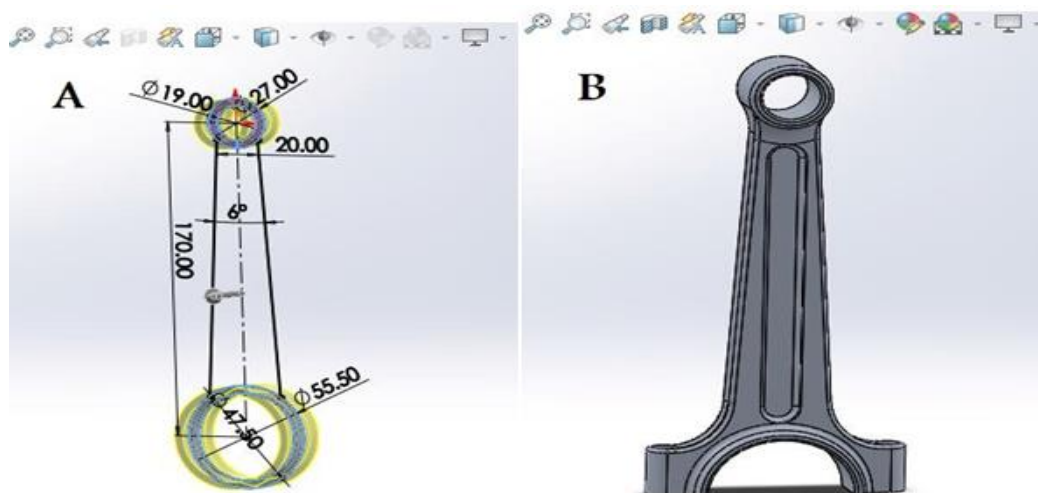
Étape de construction d'une forme 3D de la bielle
